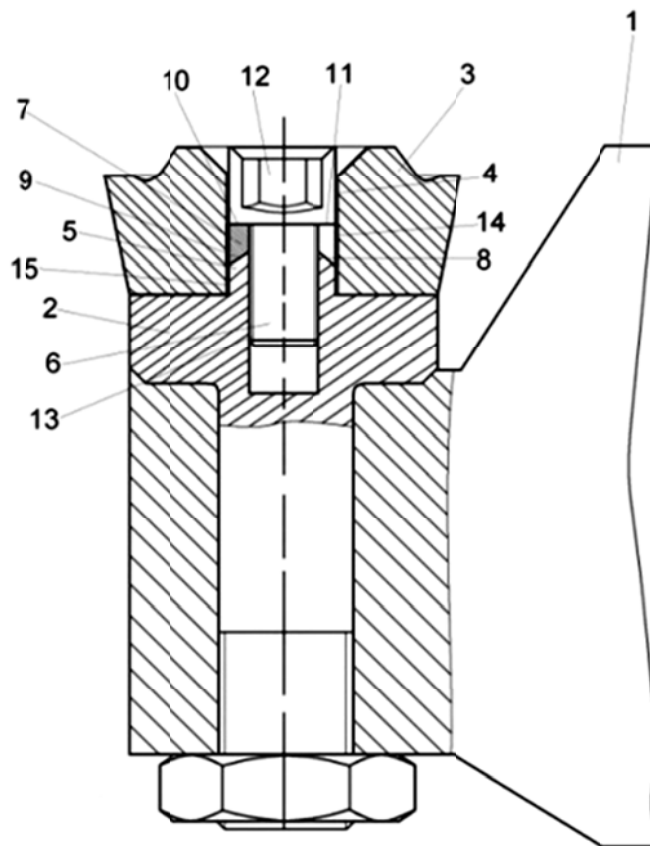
Усовершенствованная конструкция сборного чашечного резца (патент № 32230)
